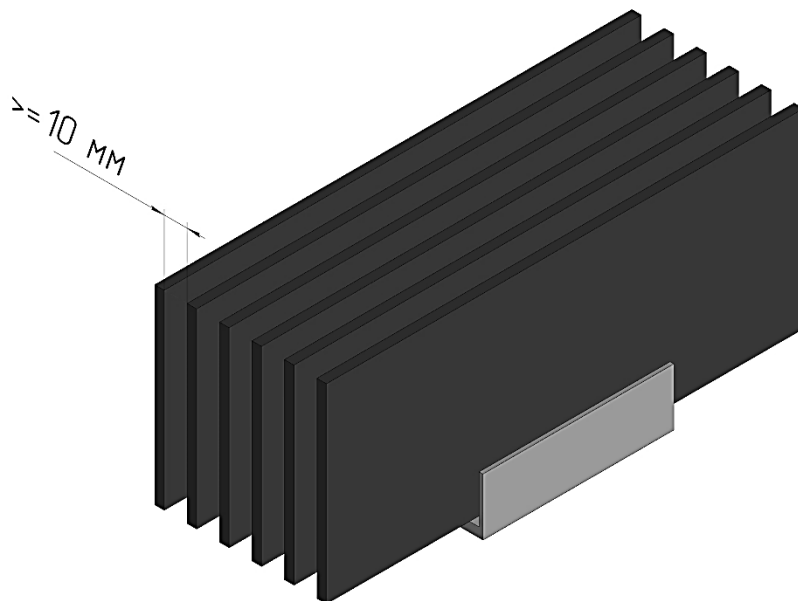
Схема укладки исходных заготовок в электропечи для нагрева
